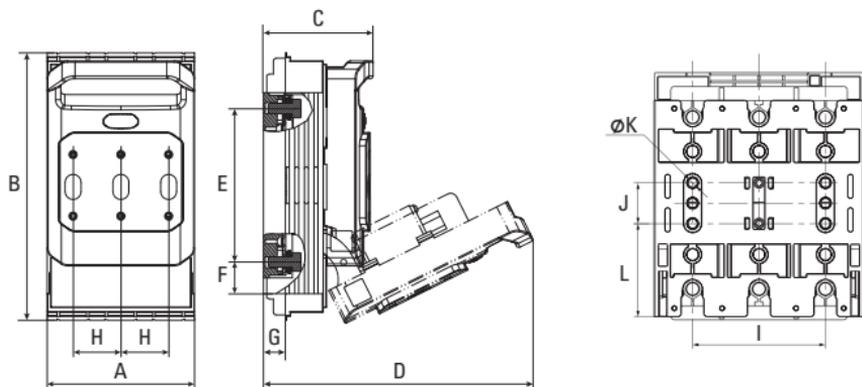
Габаритные размеры выключателя-разъединителя УВРЭ v2 160 А ЕКФ
